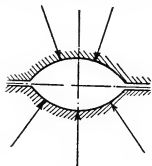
Схема расположения месдоз в валках для прокатки овального профиля
